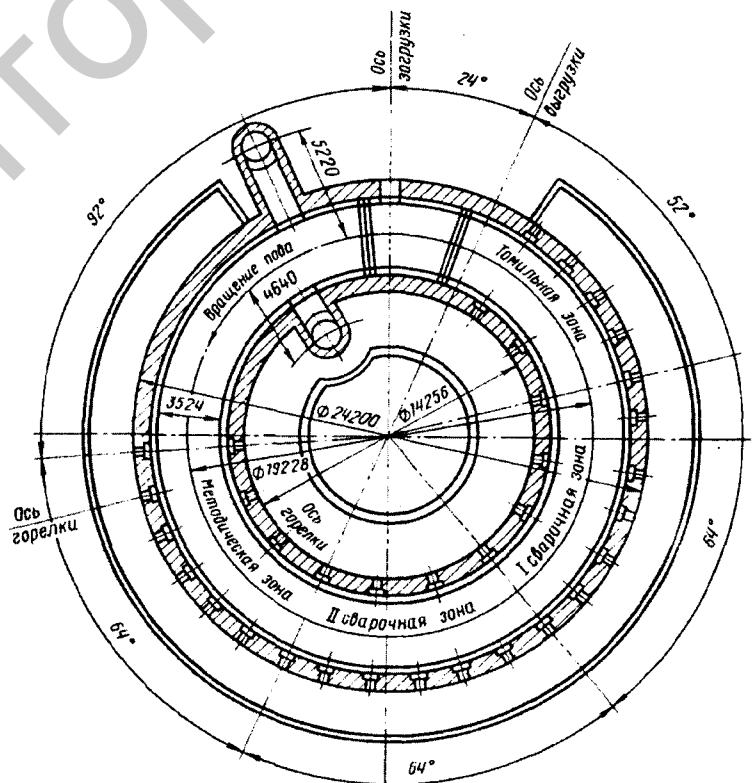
Схема кольцевой печи для нагрева трубных заготовок
